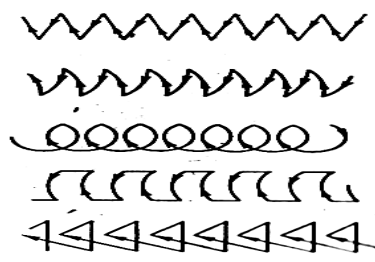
Схемы движения электрода при ручной электродуговой сварке.
